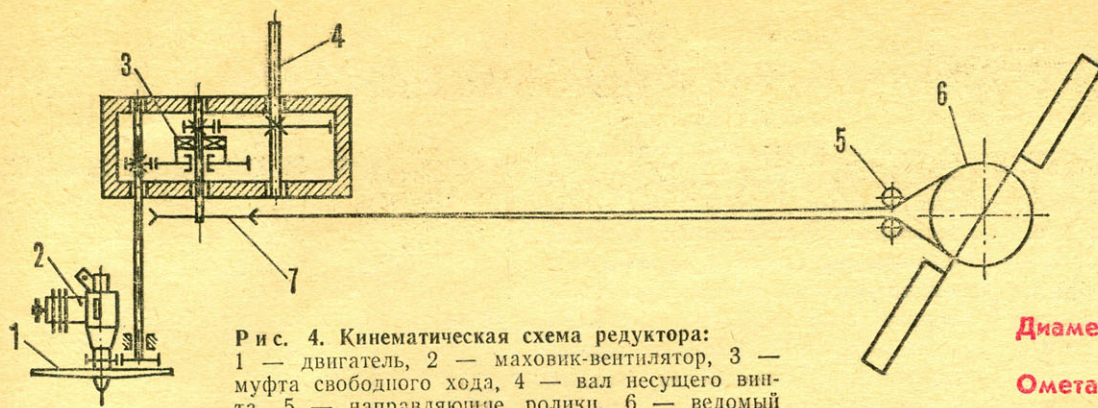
Кинематическая схема редуктора: 1 — двигатель, 2 — маховик-вентилятор, 3 — муфта свободного хода, 4 — вал несущего винта, 5 — направляющие ролики, 6 — ведомый шкив, 7 — ведущий шкив.
